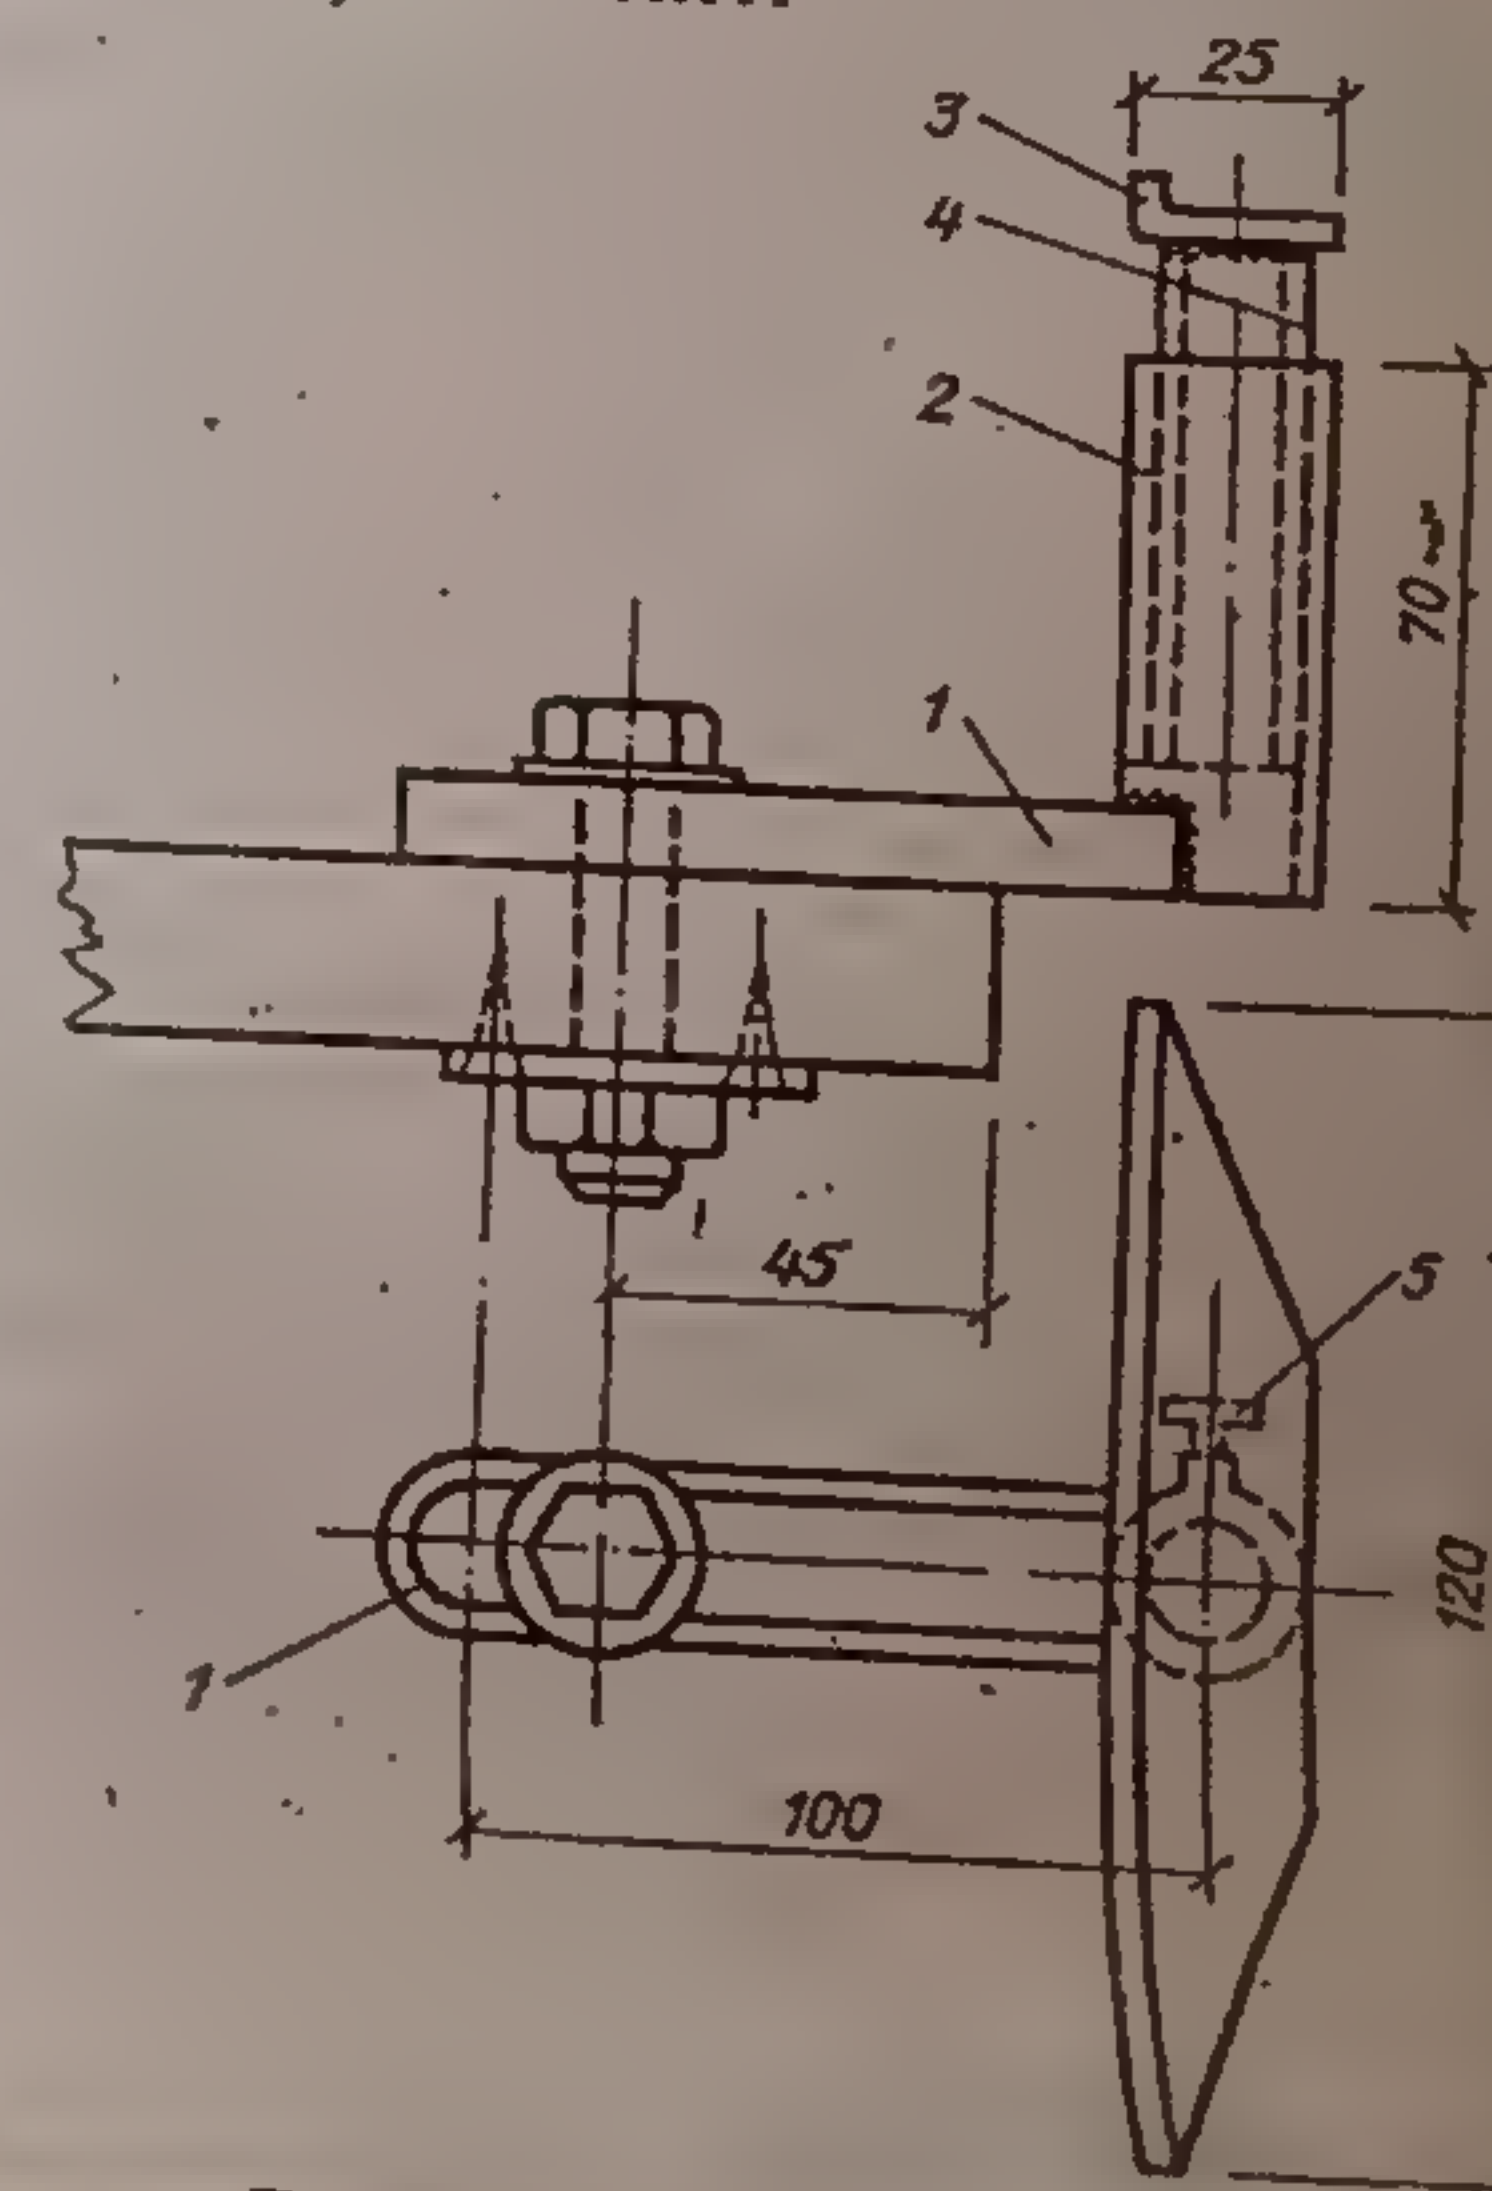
Приспособление для упора резца: 1 — скоба; 2 — прут; 3 — упор (уголок); 4 — прут; 5 — стопорный винт.
